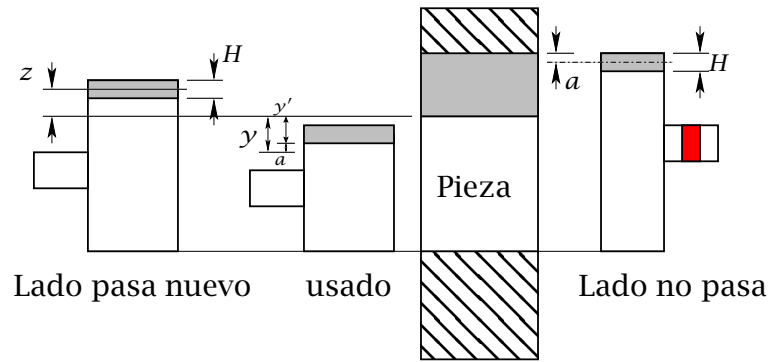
Límites de tolerancia de un calibre tampón para dimensiones superiores a 180 mm.
